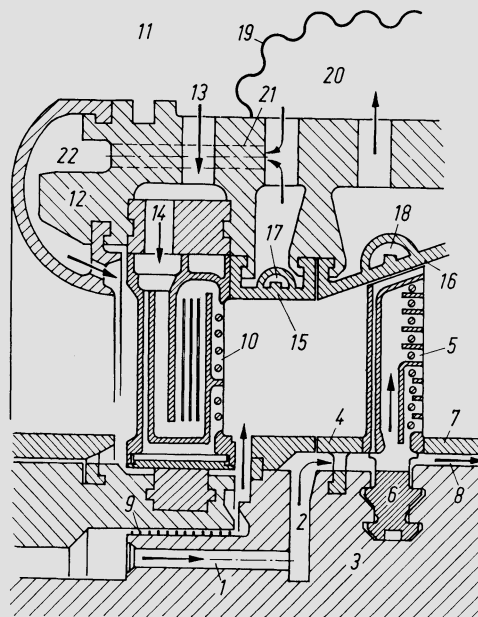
Kühlluftführung bei einer Gasturbine mit Trommelrotor (BBC)
